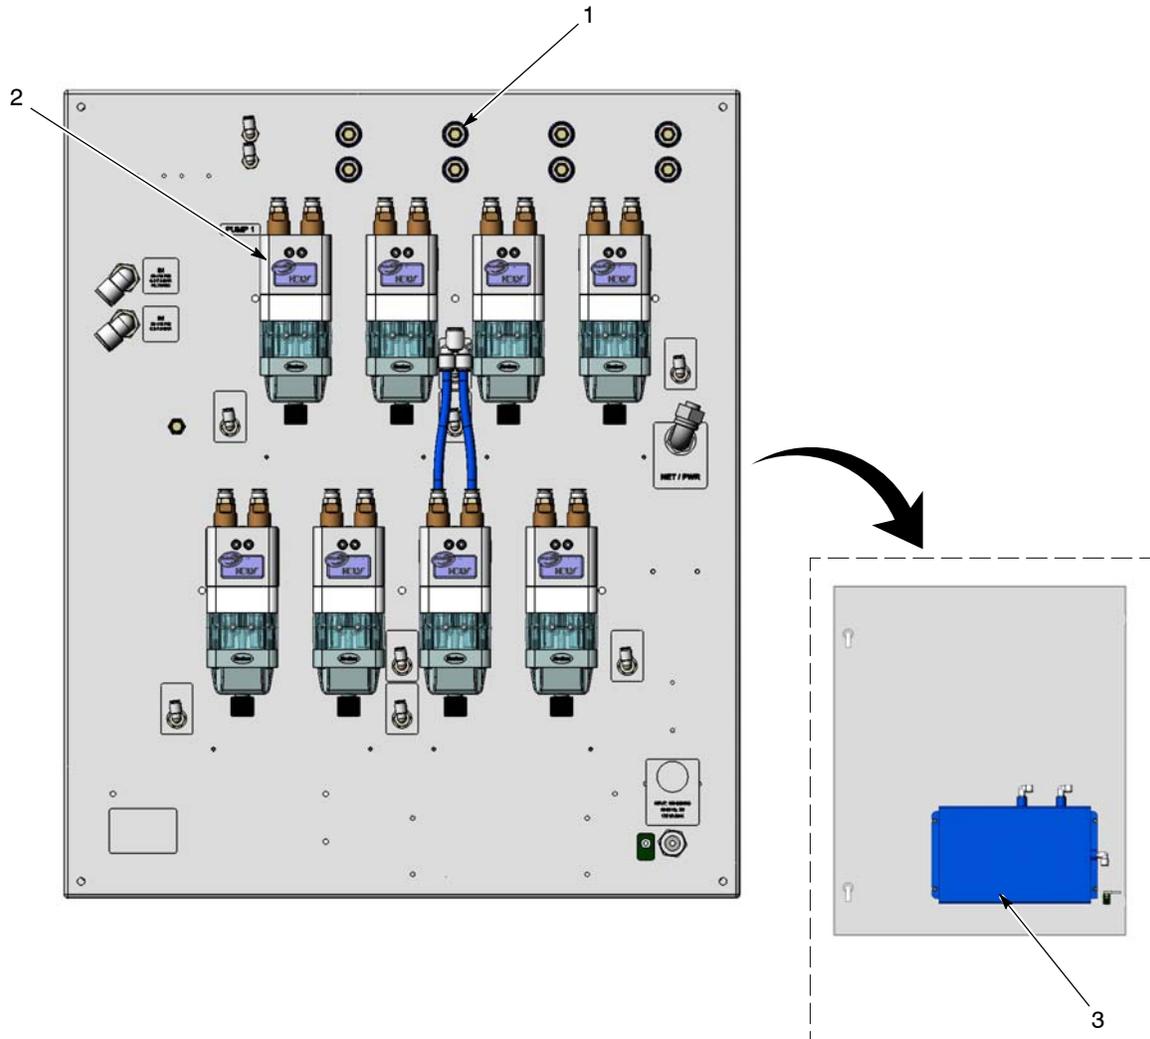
Externe Ersatzteile der Pumpenkonsole (Abb.: Konsole für acht Pumpen)
